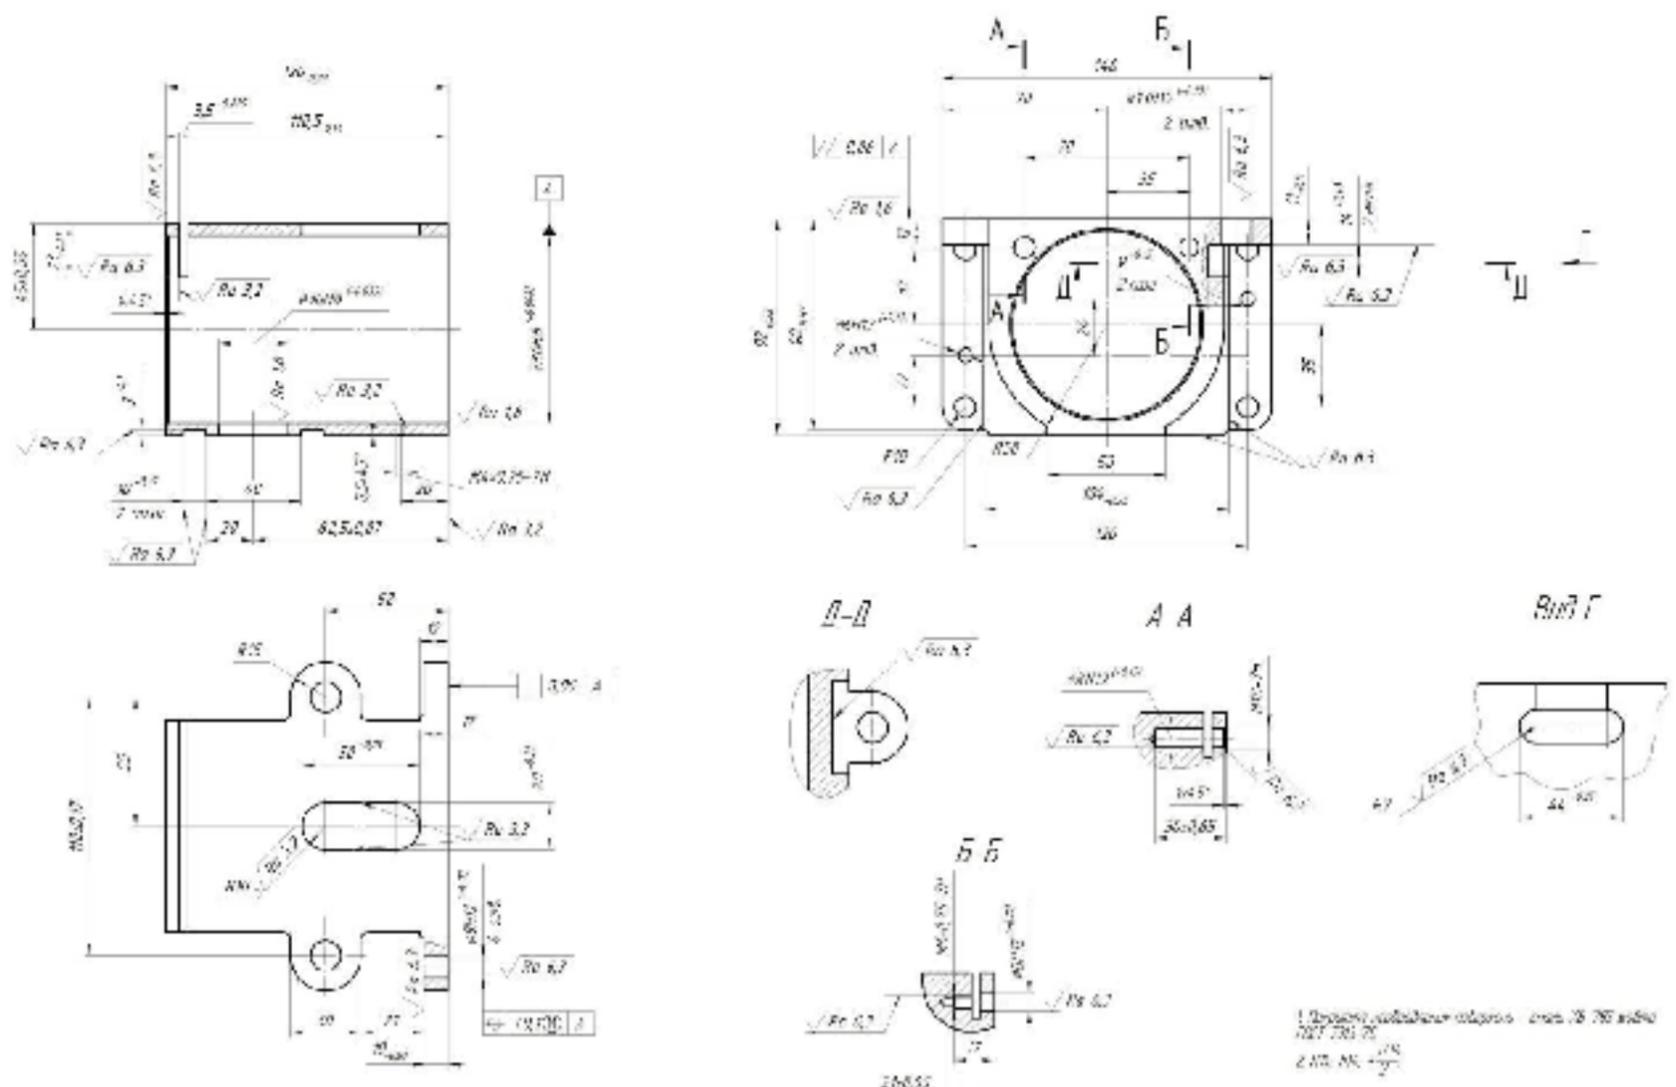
Ескіз деталі «Корпус БР.36.004»
